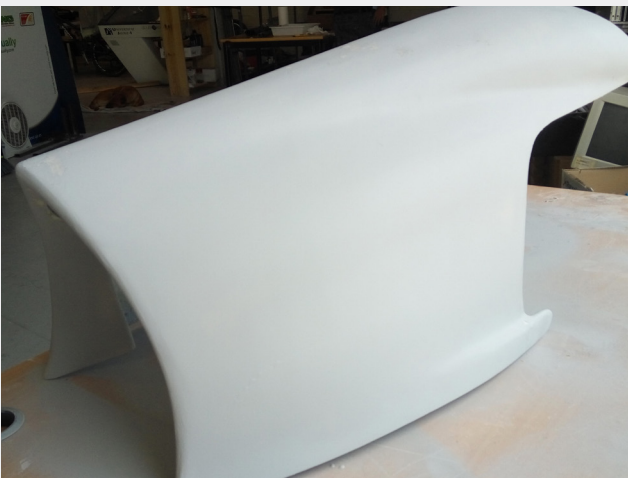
Detalle de la quilla tras la operación de aparejado.
